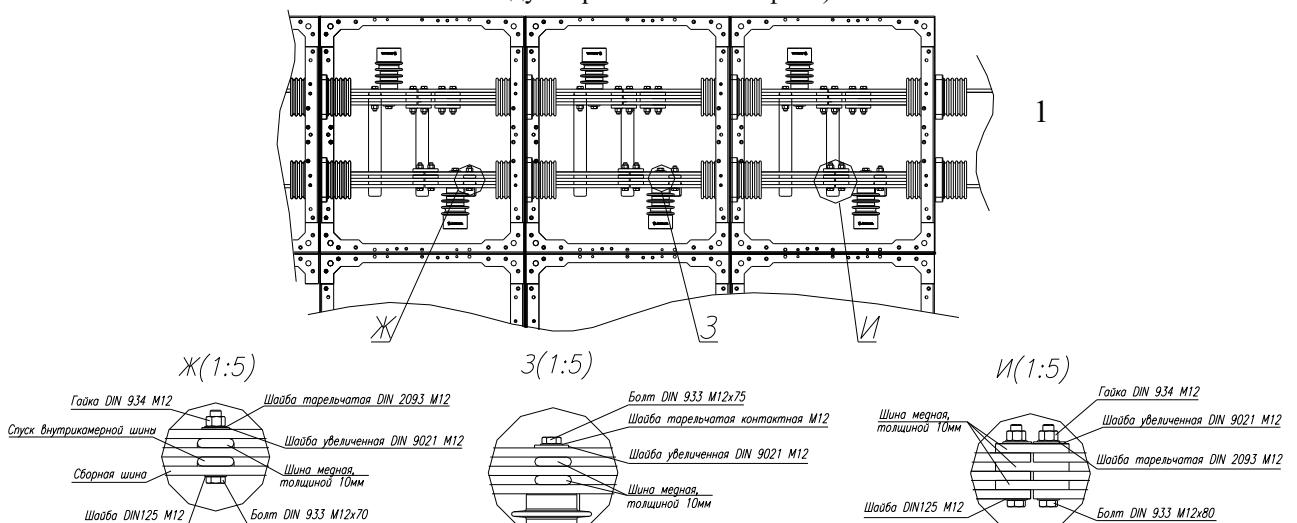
Монтаж сборных шин 3150; 4000А (вид сверху на шкафы КРУ)
